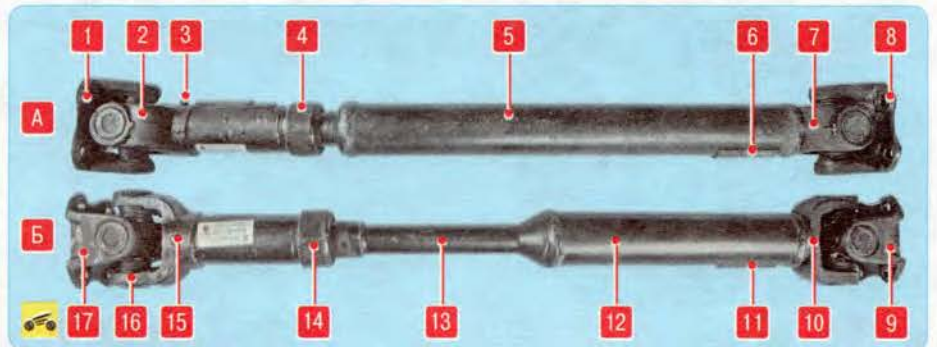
Карданные валы: А – задний карданный вал; Б – передний карданный вал; 1, 9 – передние фланцы; 2, 16 – скользящие вилки; 3, 15 – пресс-масленки; 4, 14 – обоймы; 5, 12 – трубы карданных валов; 6, 11 – балансировочные пластины; 7, 10 – вилки карданных шарниров; 8, 17 – задние фланцы; 13 – участок вала уменьшенного диаметра
